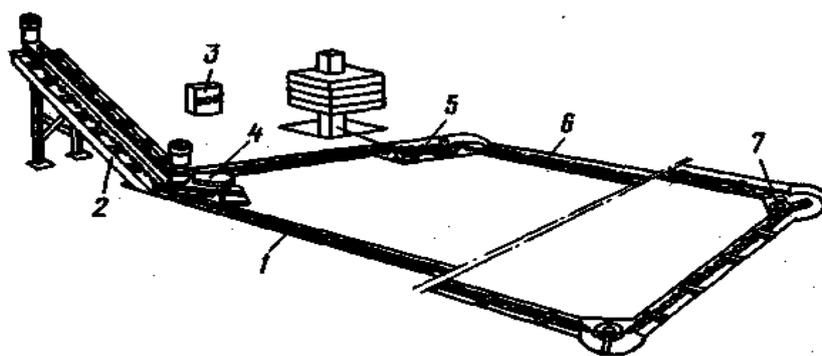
Транспортёр скребковый навозоуборочный ТСН-160А:
